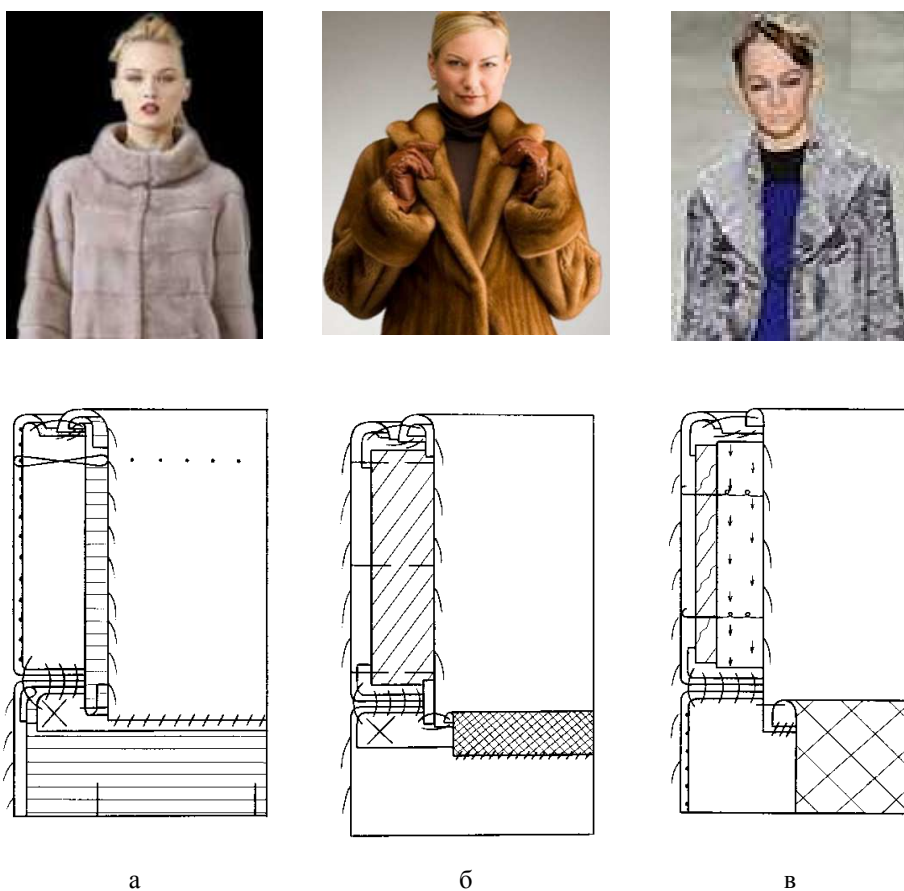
Монтажная схема конструкции воротника: а – соединение верхнего воротника с нижним из кожи или замши; б – вариант обработки воротника и соединение его с горловиной в изделиях из дорогостоящего меха; в – вариант обработки воротника и соединение его с горловиной в изделиях из менее дорогостоящих видов ПМП
